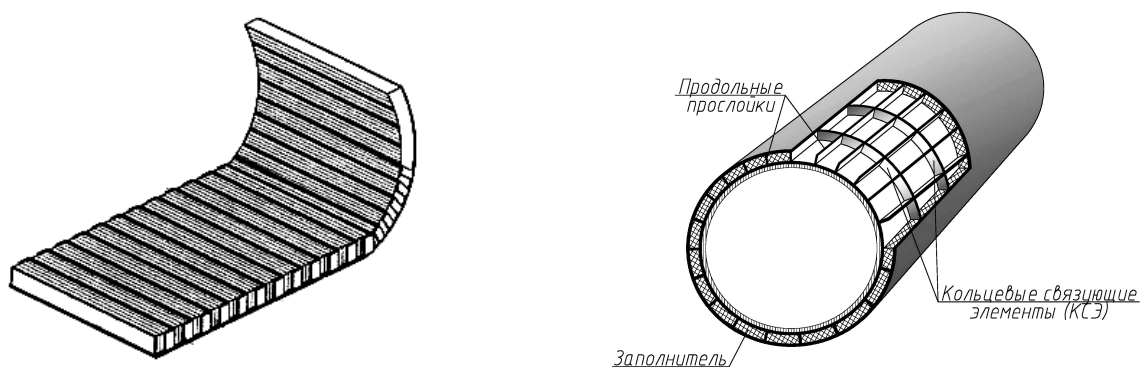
Конструкционно-теплоизоляционный элемент и оболочка с наполнителем на его основе
